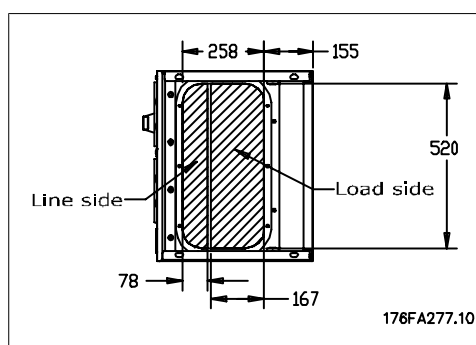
Кабельный ввод преобразователя частоты (вид снизу) - корпус E1.
